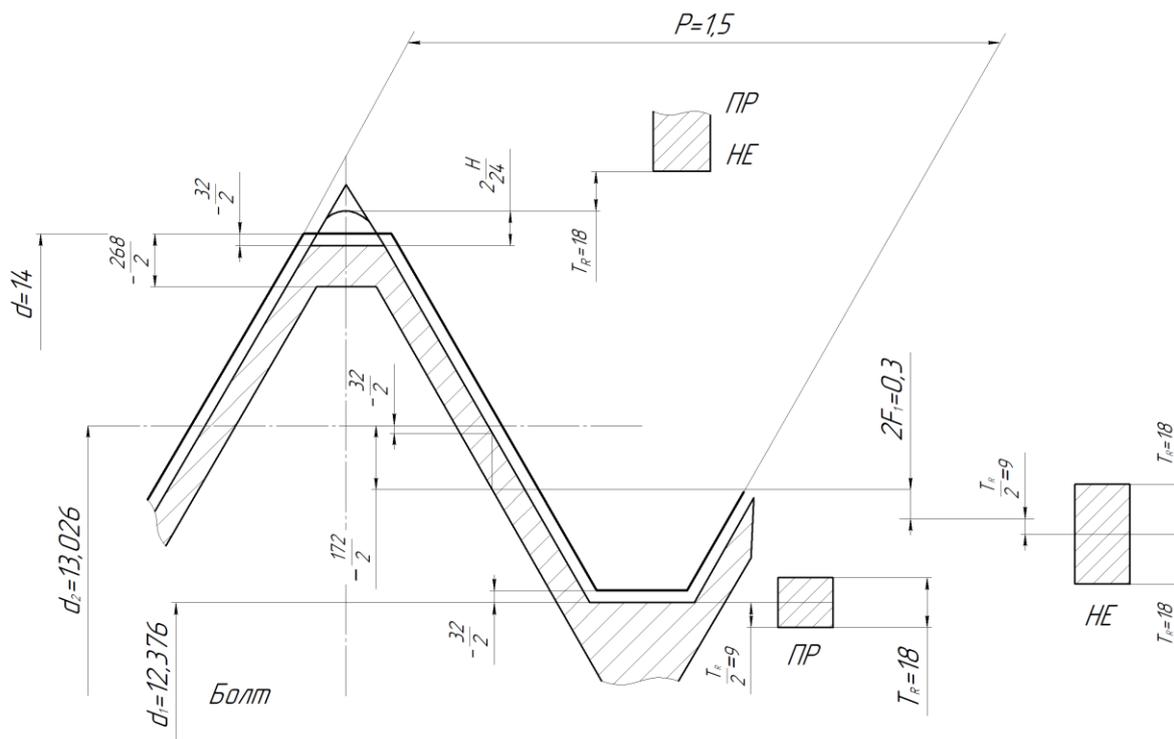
Схема расчета полей допусков резьбового калибра – кольца
